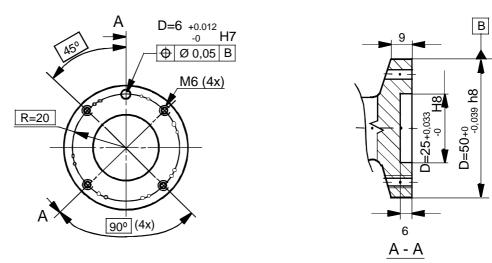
Interfaz mecánica y brida de montaje (dimensiones en mm).
